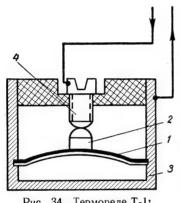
Термореле Т-1: 1— биметаллическая мембрана; 2— контакт; 3— кожух; 4— винт регулировочный
